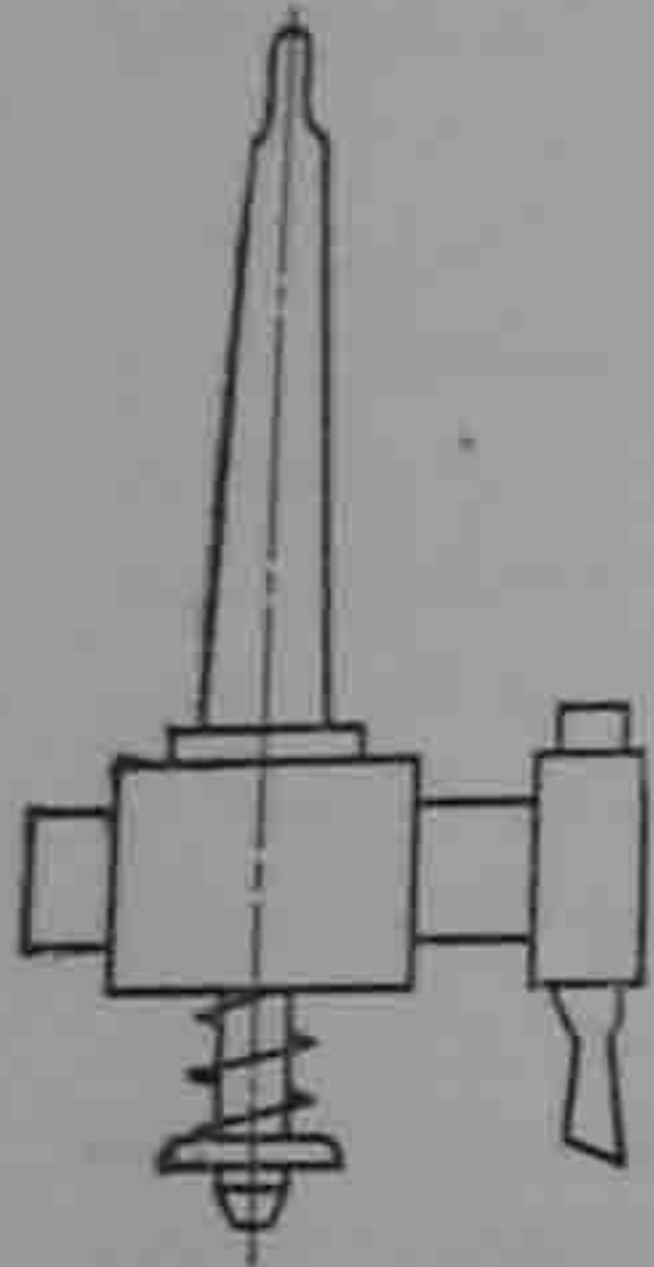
Схема головки для кольцевого сверления (циркулярный резец)
